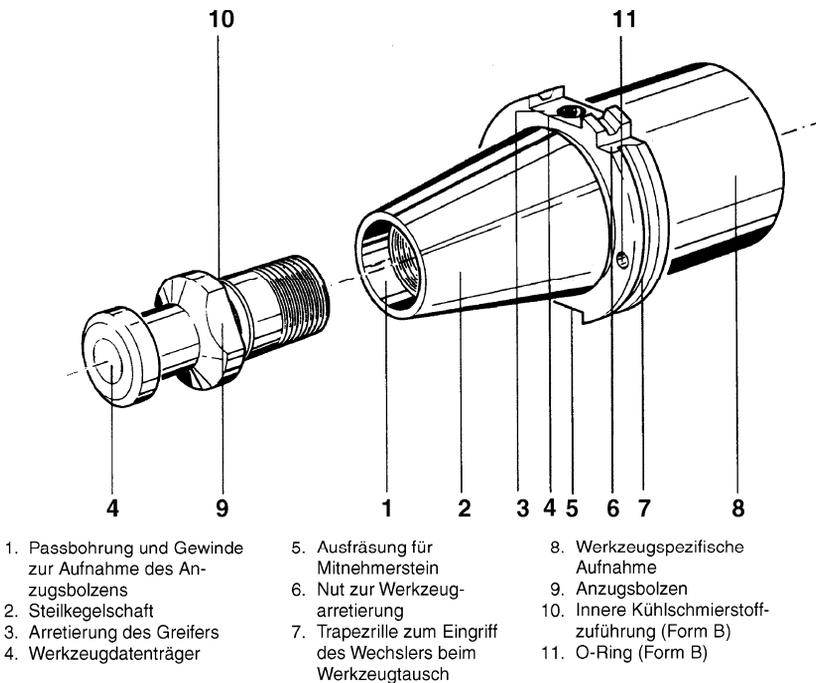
Steilkegelschaft für Werkzeuge mit Steilkegel 7:24 für automatischen Werkzeugwechsel (DIN 69871). Die Trapezzille 7 ermöglicht die Betätigung durch einen Werkzeugwechsler. Ein Werkzeugdatenträger ermöglicht die Kennung des jeweiligen Werkzeuges für den Datenspeicher der CNC-Steuerung der WZM. (Quelle: Deckel, München)
